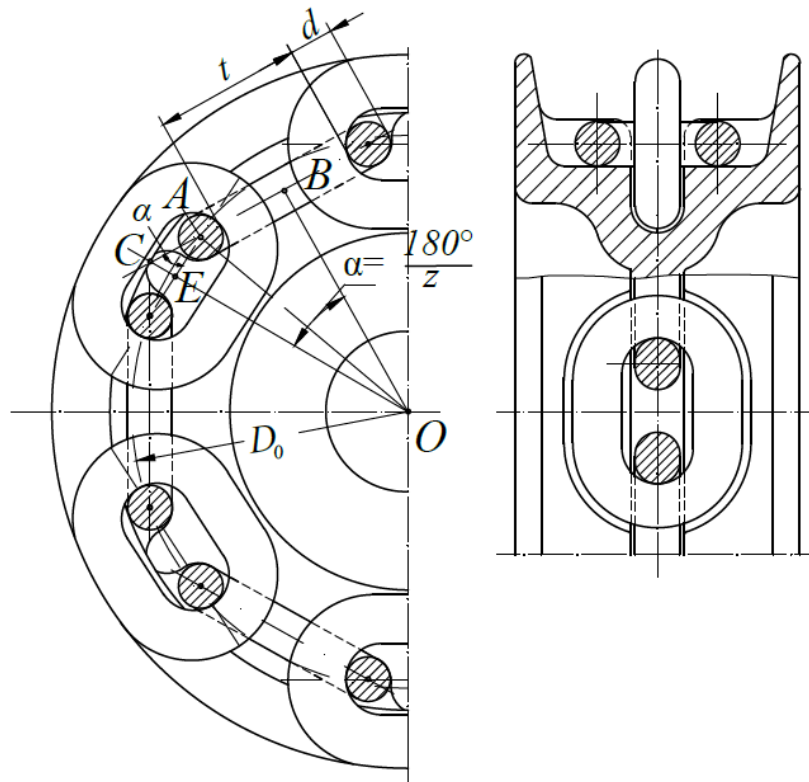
Звездочка для калиброванной сварной цепи
